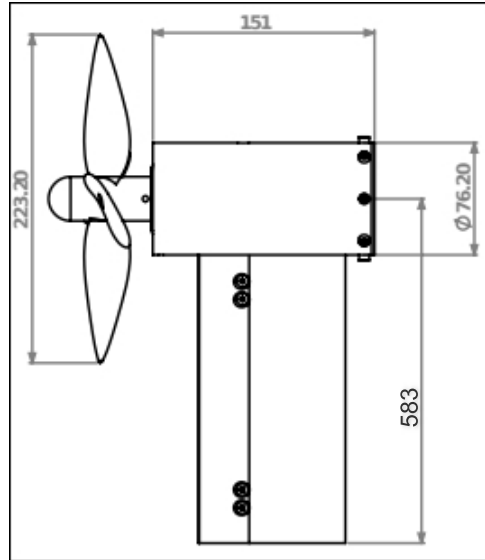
Desenho técnico com dimensões em milímetros - Mendes (2020)
